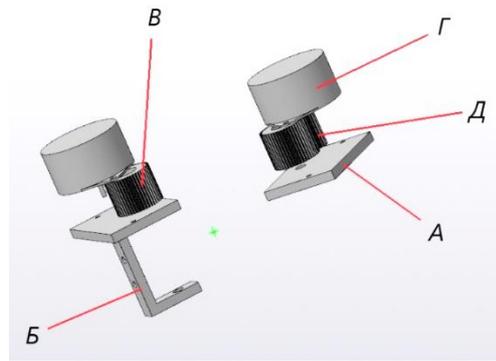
3D-модель крепления шаговых двигателей: А — стойка под шаговые двигатели; Б — упорная стойка; В — регулировочная шестерня; Г — шаговый двигатель; Д — ведущая шестерня
